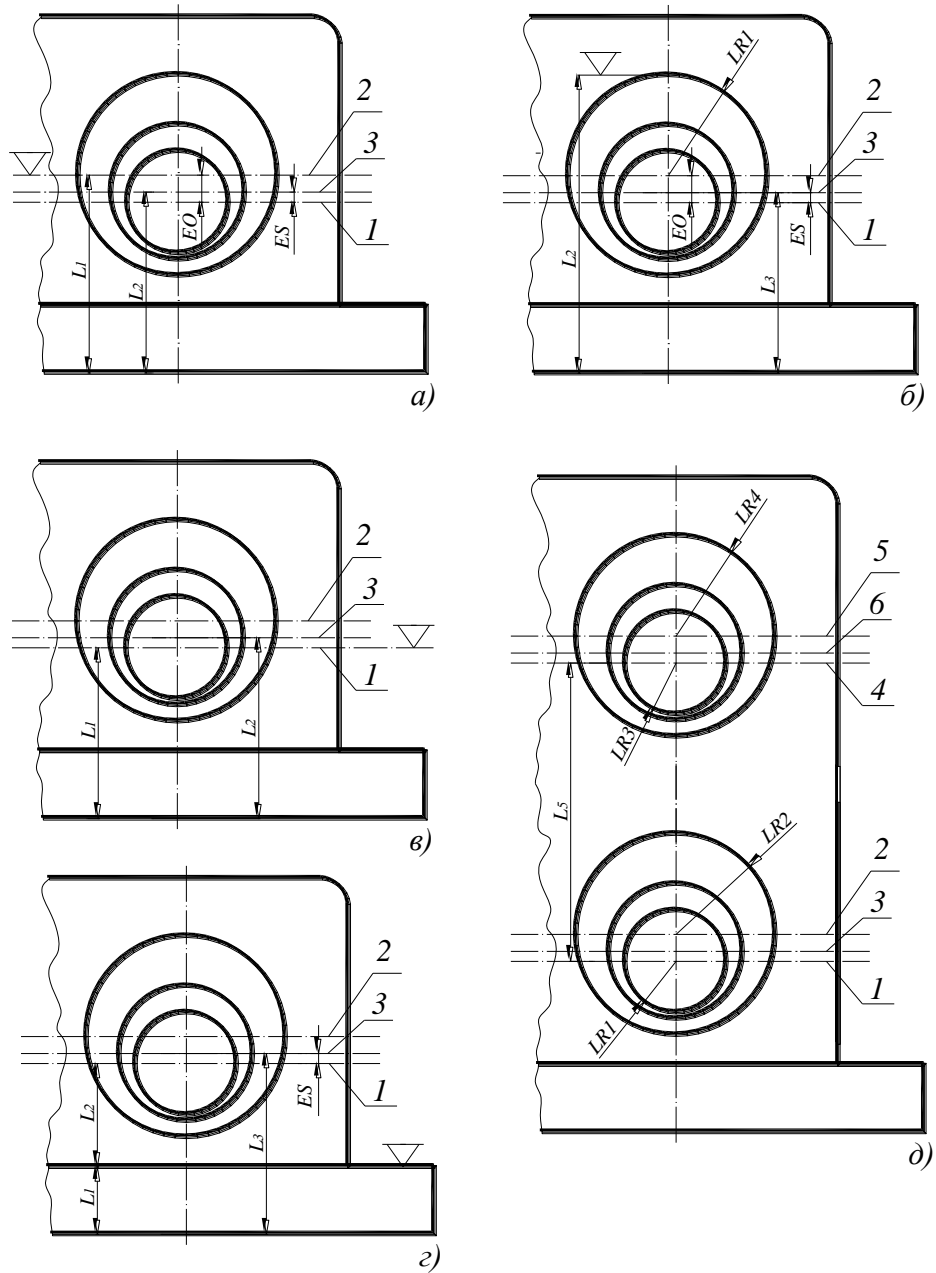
Варіанти розміщення заготовки корпусного типу для здійснення різальних операцій
